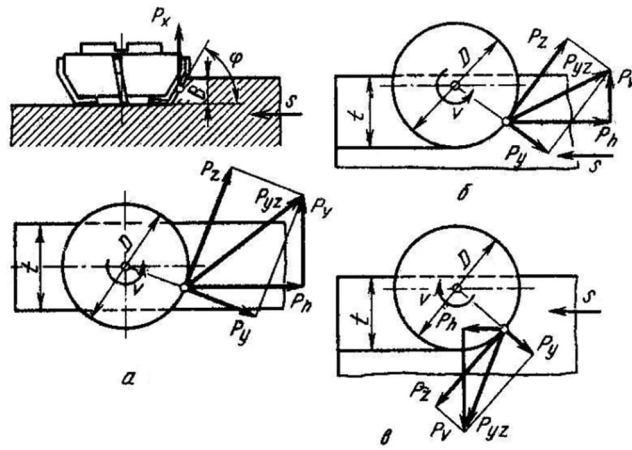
Складові сили різання при торцевому фрезеруванні:
